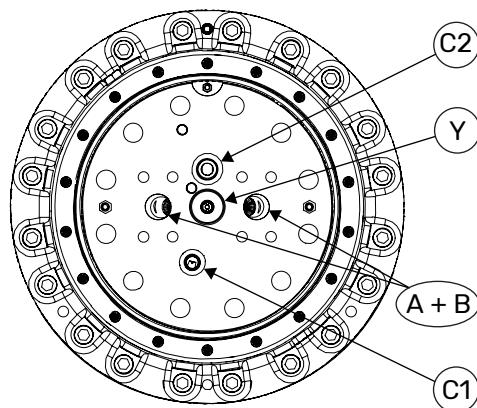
Die Hydraulikanschlüsse eines 2-Gang-C200-Motors ohne Bremse.
